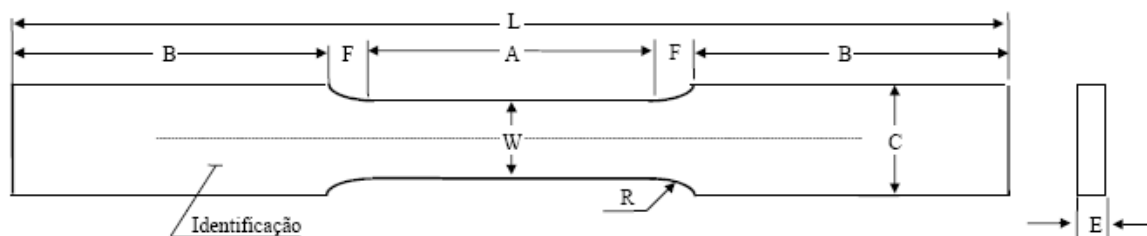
Dimensões do corpo de prova de ensaio de tração
